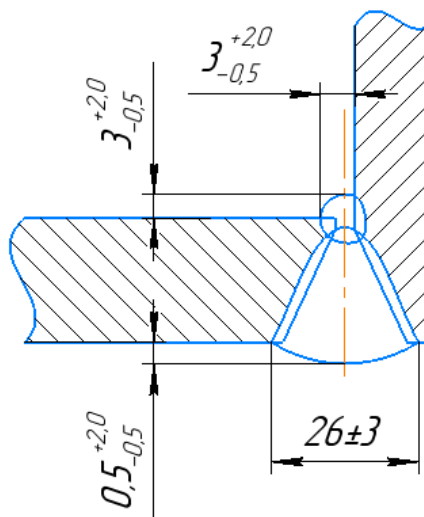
Геометрические размеры сварного шва тип сварного соединения У10 по ГОСТ 5264-80
